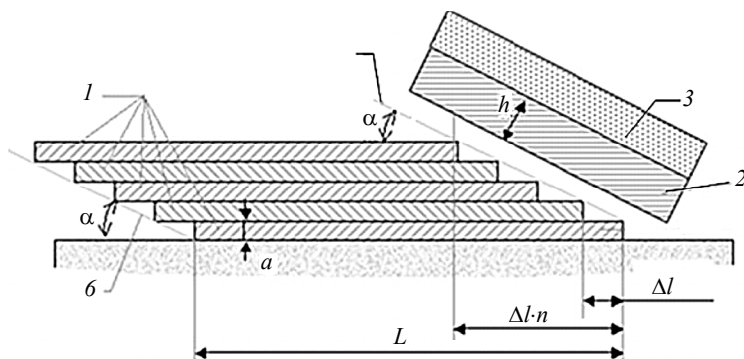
Схема сварки по торцам пакета: 1 – полосы; 2 – метаемая пластина; 3 – заряд ВВ; 4 – детонатор; 5 – плоскость выступа; b – скос; a , b , L – соответственно, толщина, ширина и длина полосы, Δl – смещение; n – количество полос
